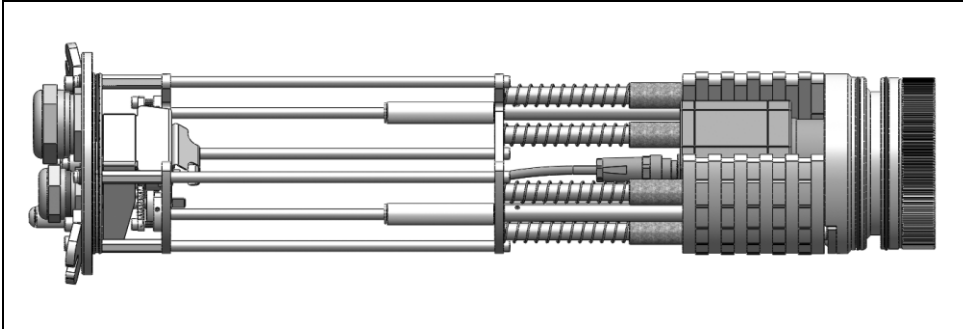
Kamera in Chassis (Cooling Jacket Advanced Extended)
